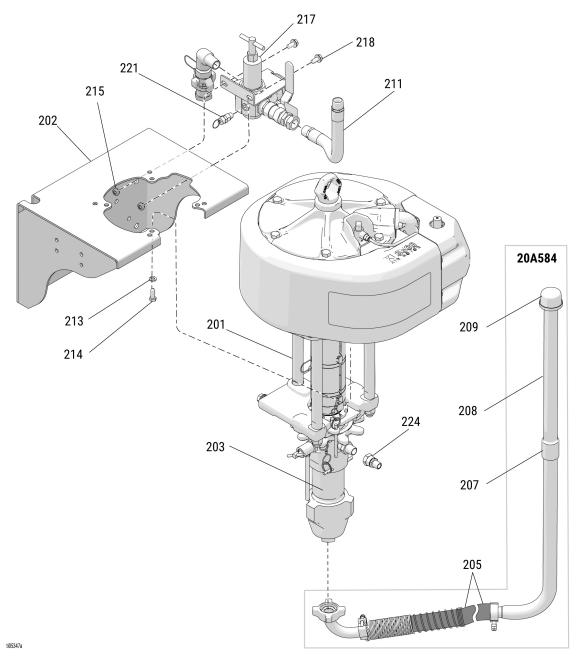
Schéma des pièces des ensembles pour montage mural
